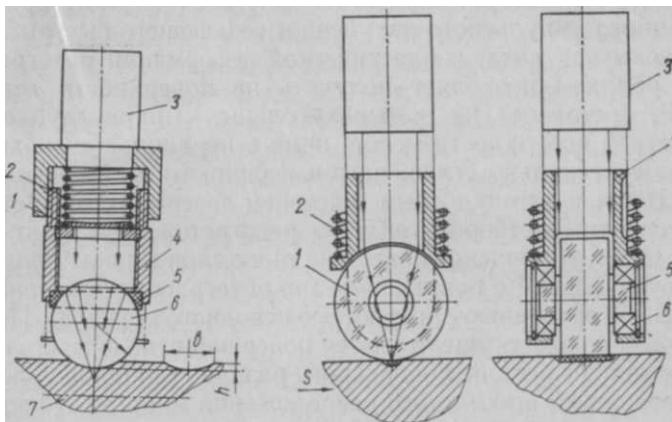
Кулькова й роликова головка для лазерного зміцнення
